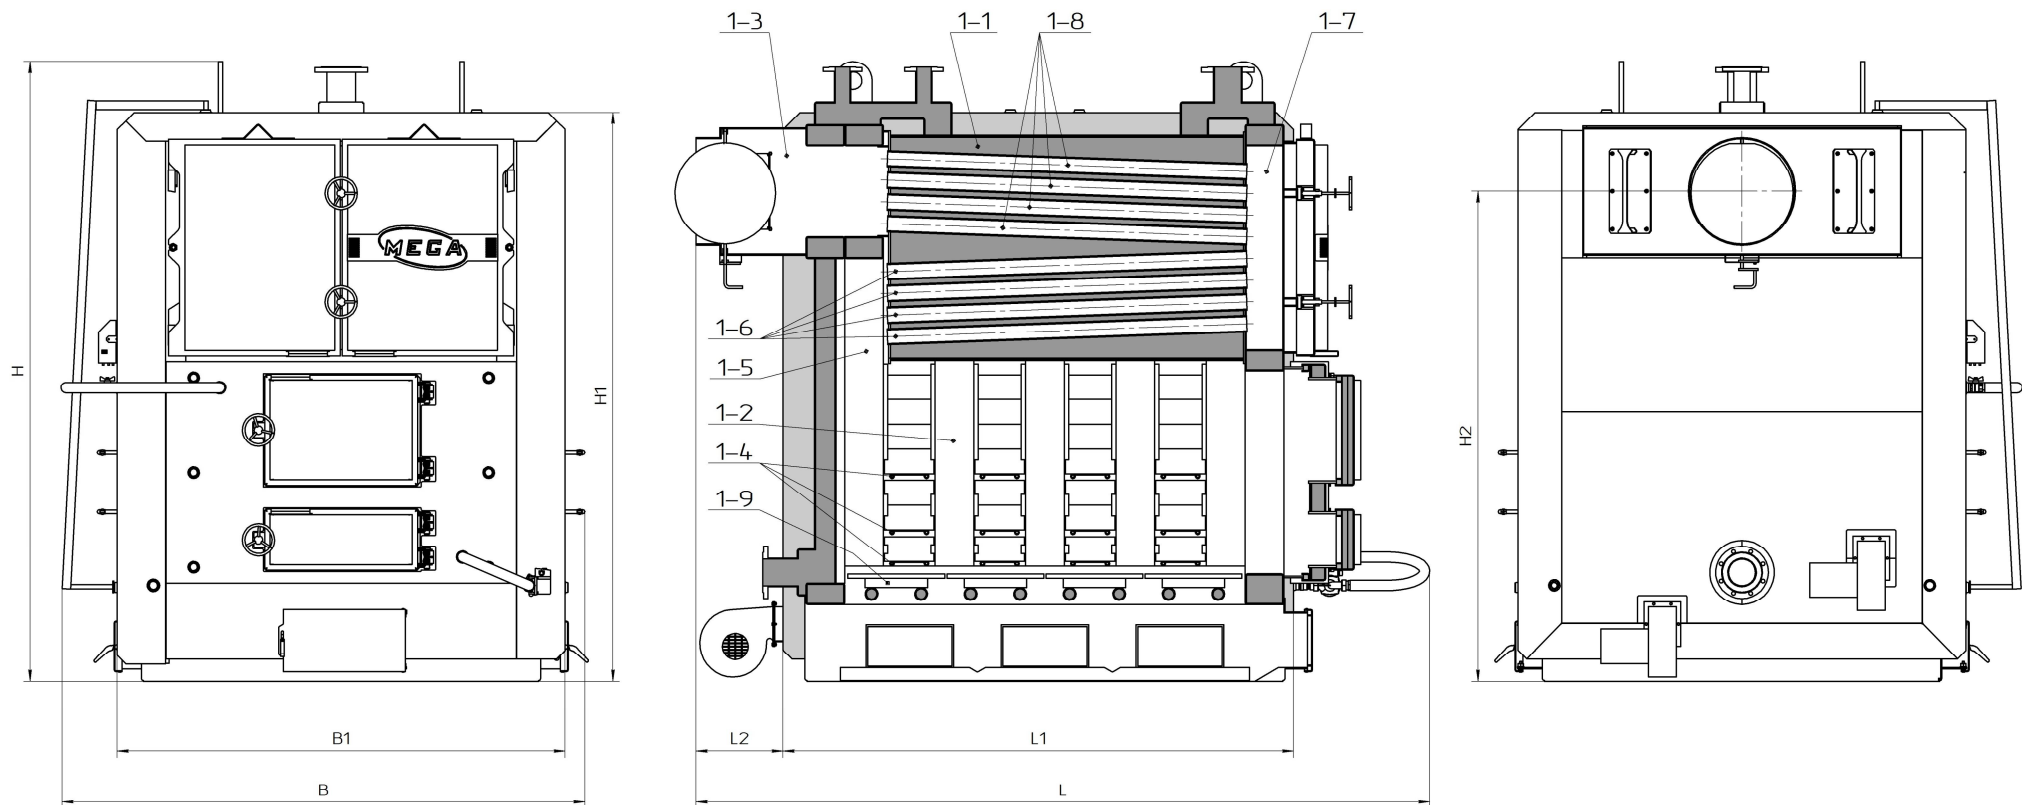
Габаритні розміри та внутрішня будова котла
